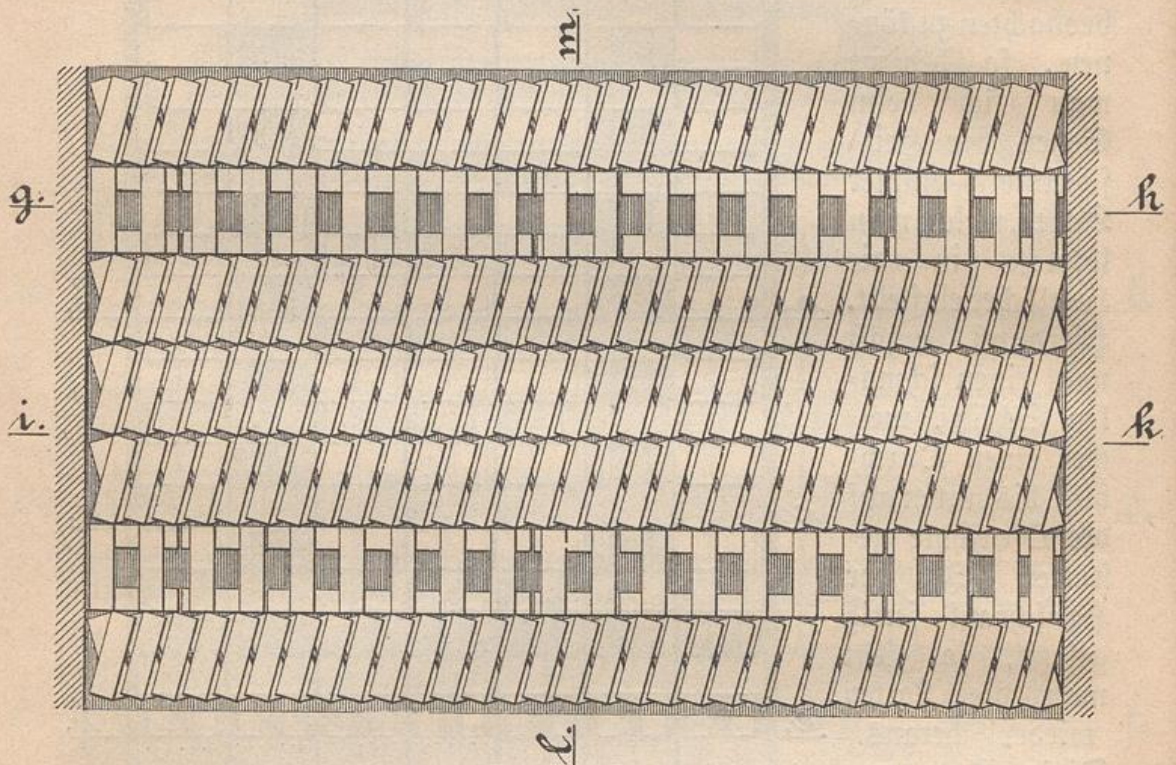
Einsatz. Grundriß. Schnitt a-b.
